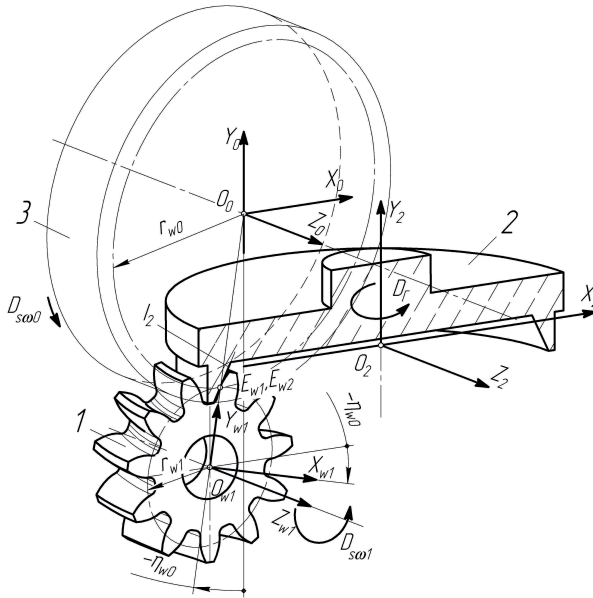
Схема установки инструмента и заготовки шестерни в станочном зацеплении
